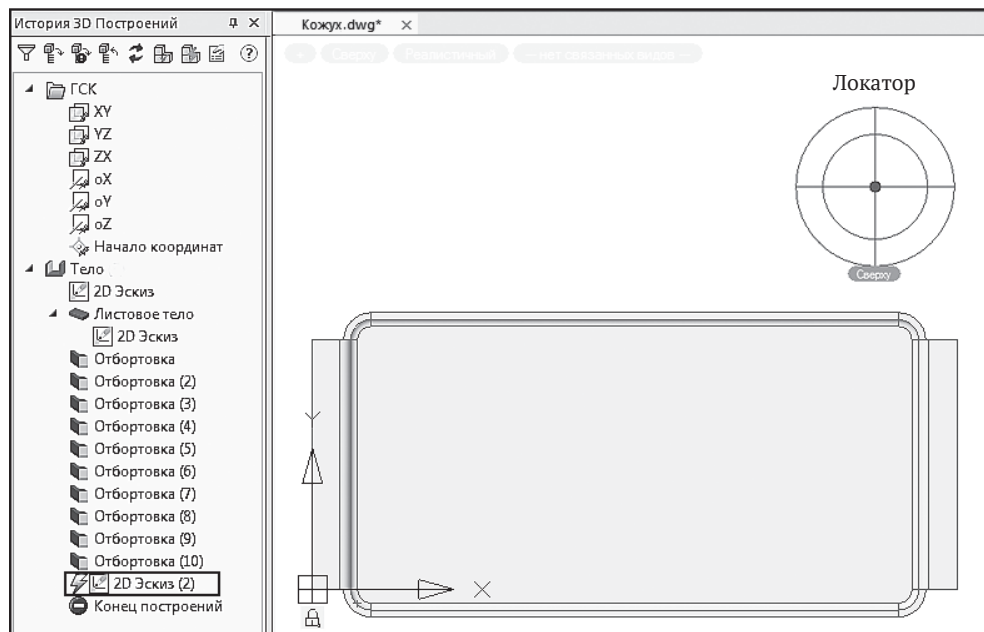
Перевод изображения 3D-модели детали к виду Вид сверху
